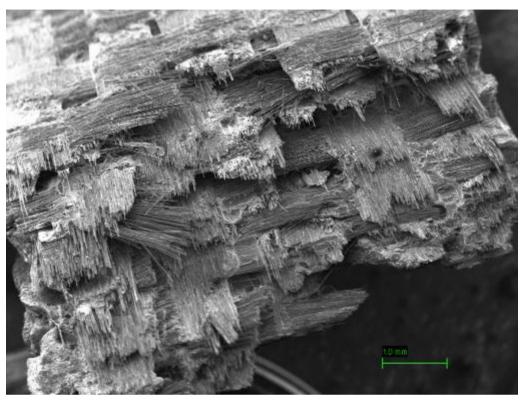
Vista frontale dell'altra superficie di frattura a basso ingrandimento (35X)
